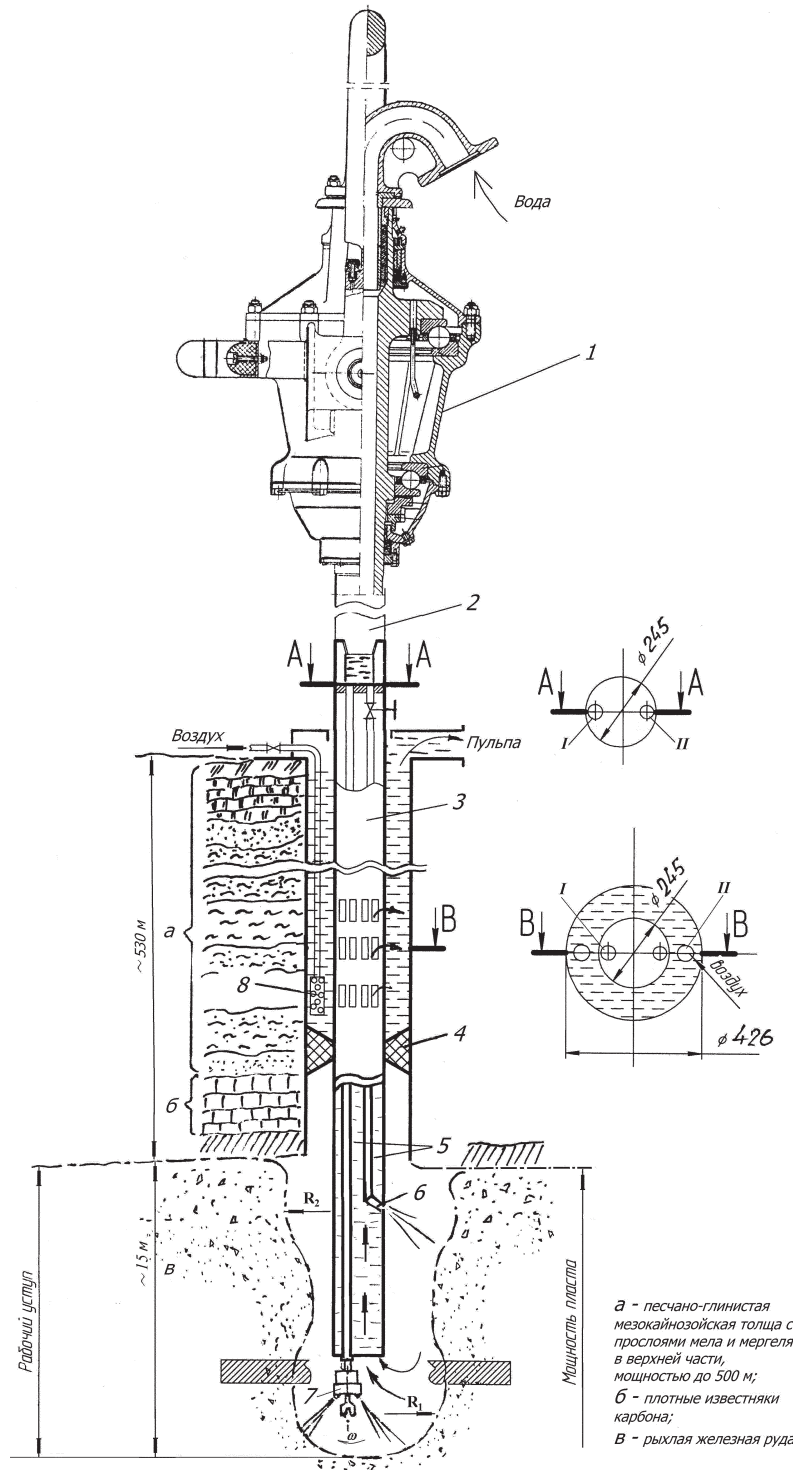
Схема гидродобывного агрегата ГДА-600 с эрлифтной установкой для подъема пульпы: 1 — вертлюг; 2 — ведущая труба; 3 — добычная колонна; 4 — пакер; 5 — трубопроводы I и II; 6 — гидромонитор; 7 — буровое долото с двумя гидромониторами; 8 — эрлифтная установка
